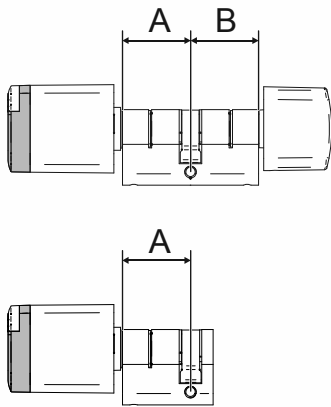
Schließzylinder: Zylinderbreite Profil EU
